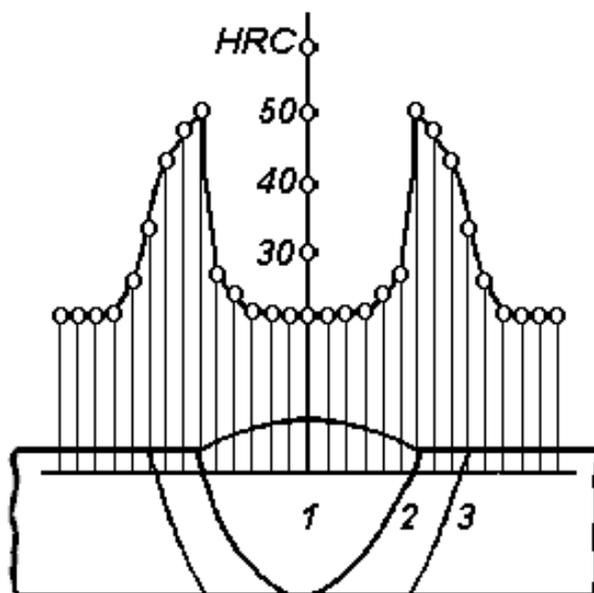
Распределение твердости по сечению сварного соединения из закаливающейся стали
